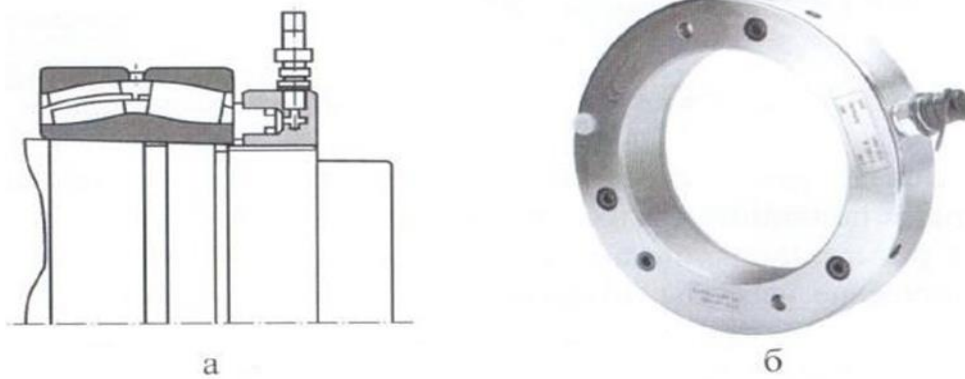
Схема встановлення підшипника за допомогою гідравлічної гайки (а) та зовнішній вид гайки серії НМV (б)
